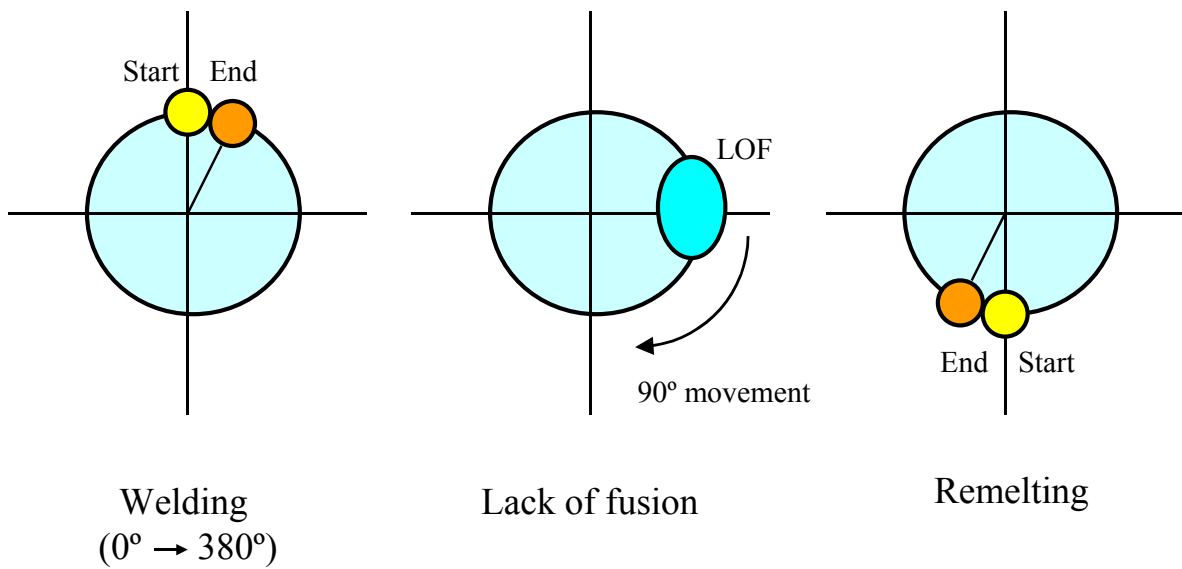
Seal tube 용접을 위한 재용융방법의 도식도
